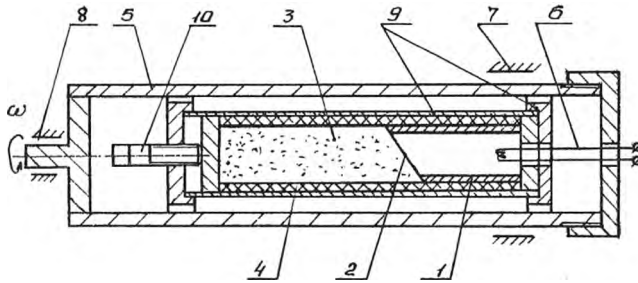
Схема получения труб в осевой опытно-технологической центробежной машине: 1 — труба; 2 — фронт горения; 3 — реакционная шихта; 4 — графитовая форма; 5 — корпус; 6 — устройство воспламенения; 7 — опоры с подшипниковым узлом (8); 9 — технологическая оснастка; 10 — инициирующее устройство
